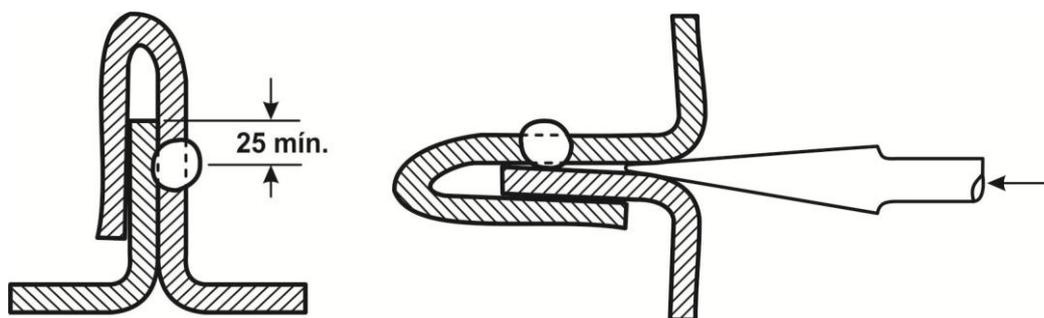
b). Esquema de ensayo para uniones entre chapas con soldadura de costura por arco.
